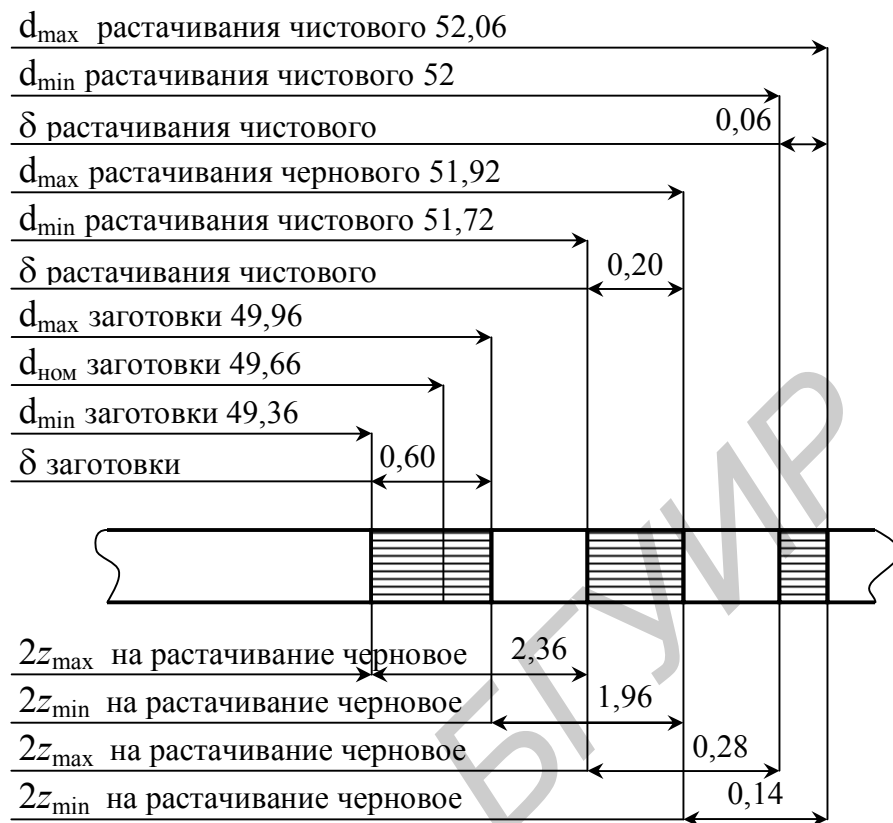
Схема расположения припусков и допусков на обработку отверстия корпуса подшипника
